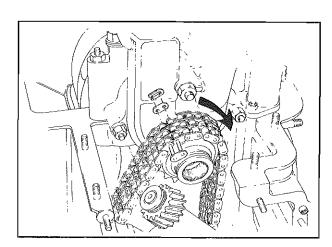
Montaggio molletta di fermo Retaining spring assembly
